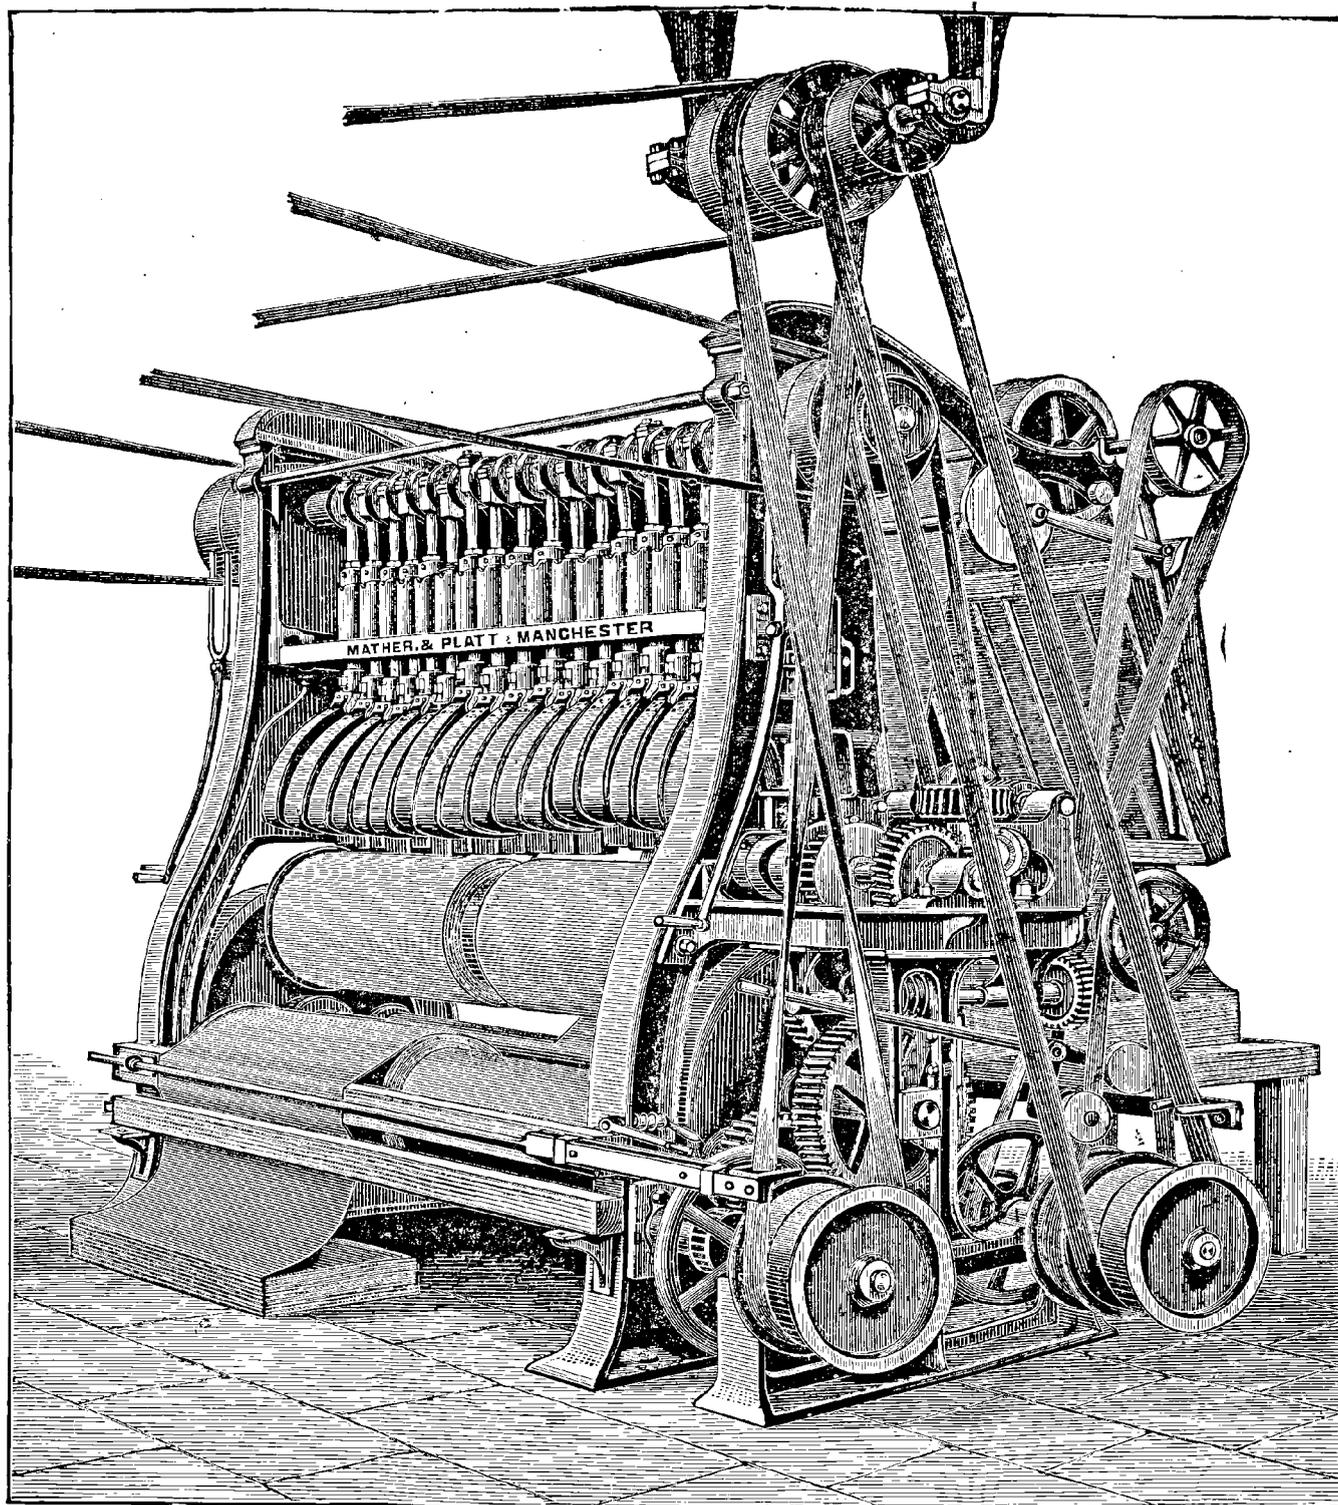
Machine à bétlier, construction Mather et Platt, de Manchester.
